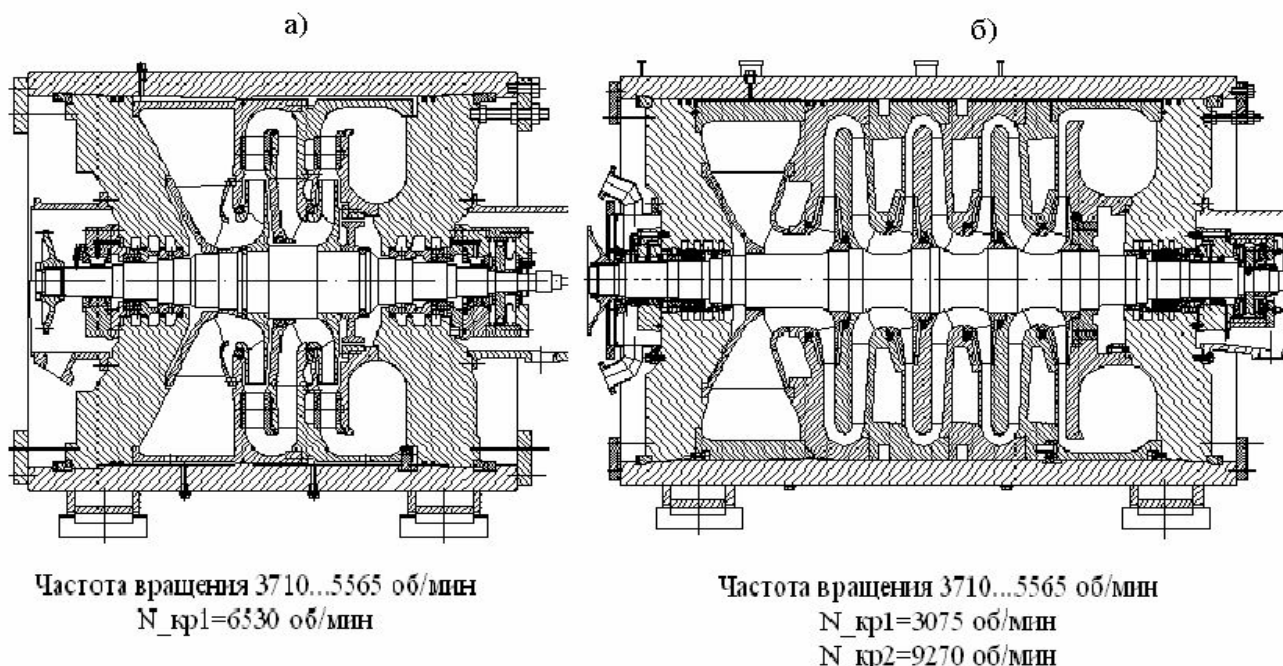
Центробежные компрессоры: а) – 291ГЦ2-395/53-76 и
